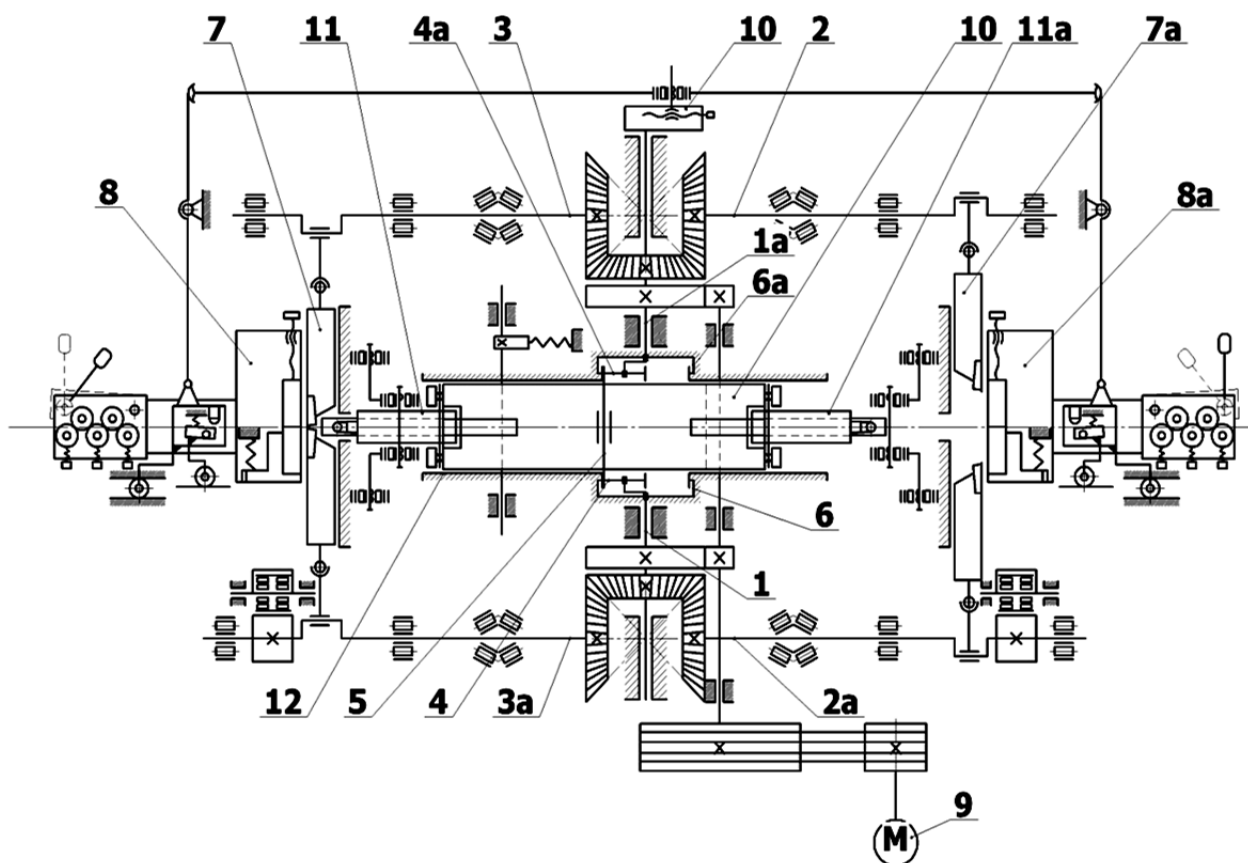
Кинематическая схема гвоздильного пресс-автомата с бесшатунным главным исполнительным механизмом
